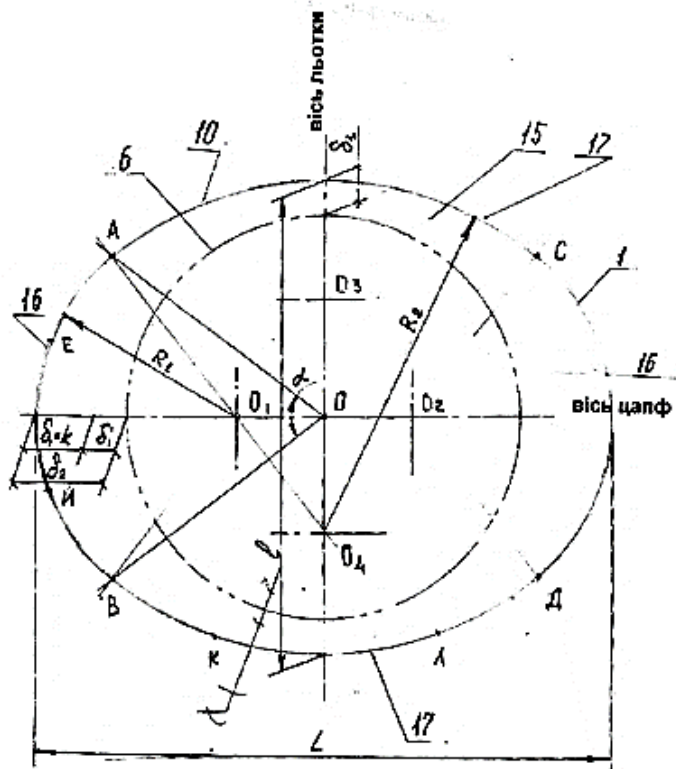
Схема контуру внутрішньої поверхні кільця опорного овальної форми
